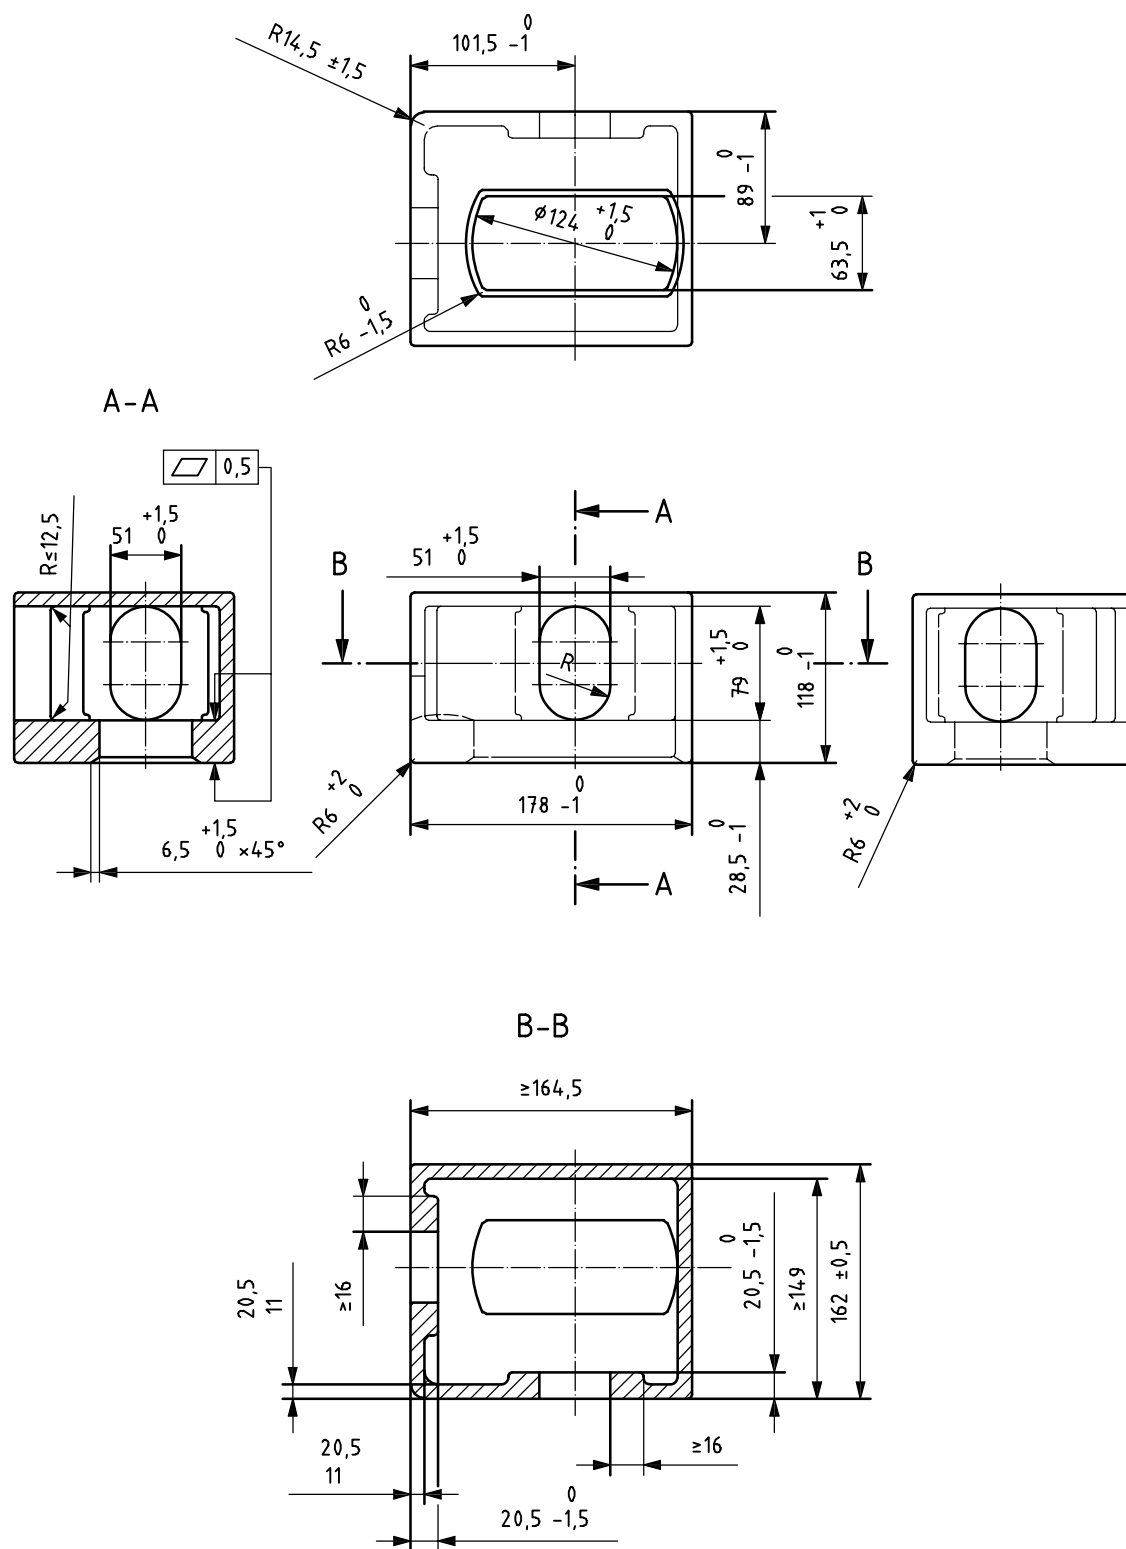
(4) 中间底角件尺寸 (单位: mm)
